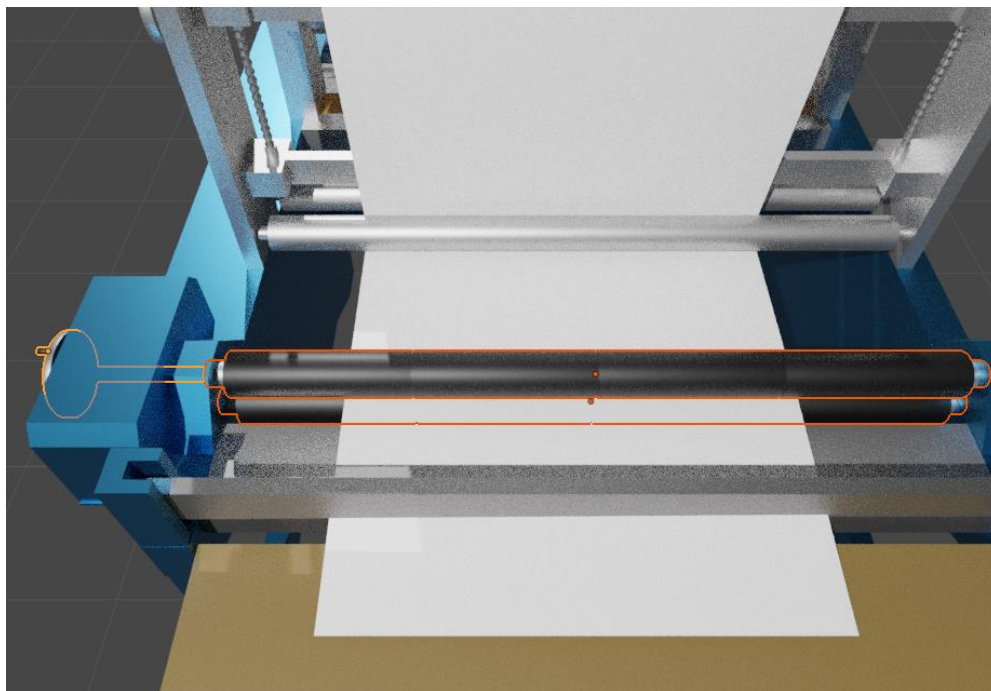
Протяжний вузол (вигляд зпереду)
